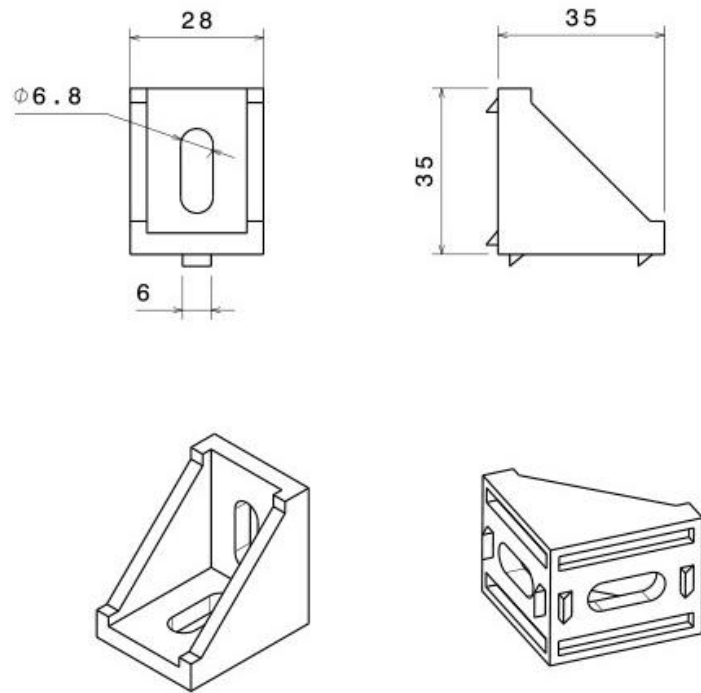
Dimensiones escuadra de fundición de aluminio para perfil de aluminio de 30x30 mm
